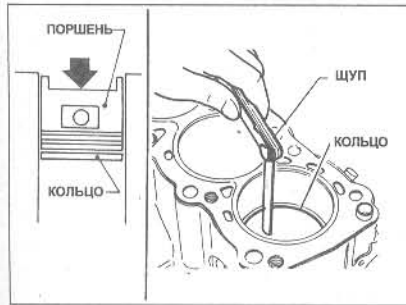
Проверка зазора разреза поршневого кольца (Глава 9)
